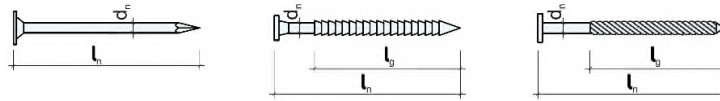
Schaftausbildung: glattschaftiger Nagel, Rillen- und Schraubnagel
